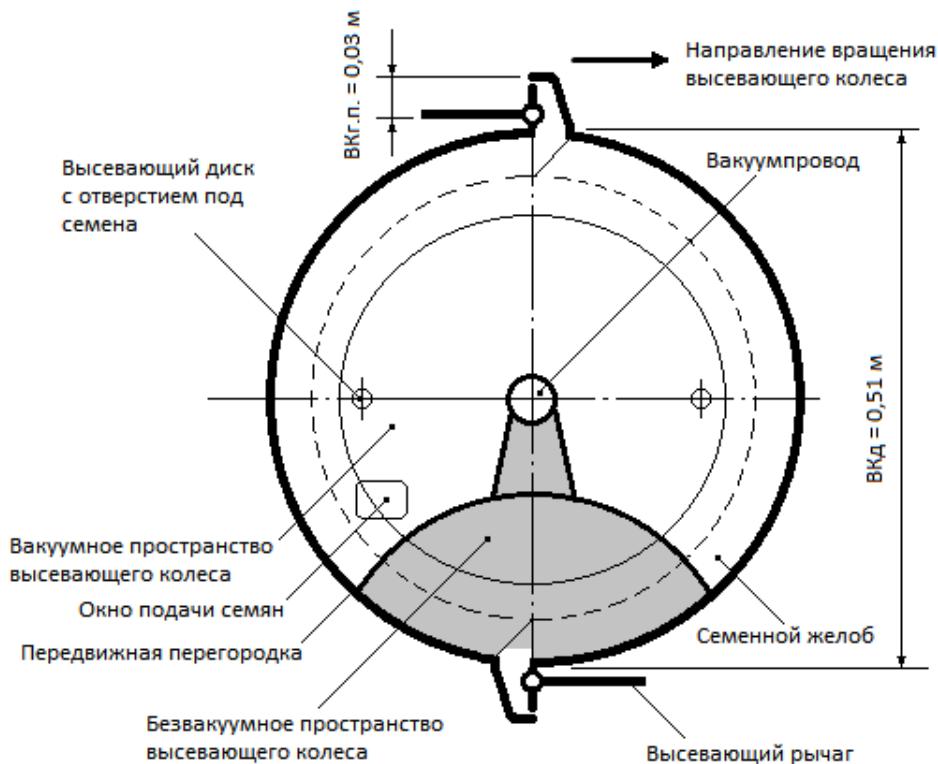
Основные конструктивные размеры высевающего колеса
